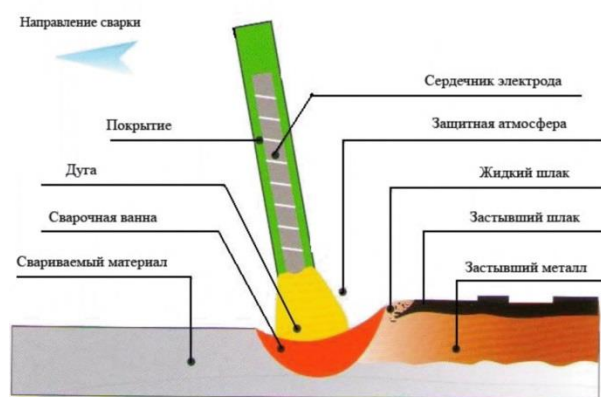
Схема ручной дуговой сварки штучными электродами
